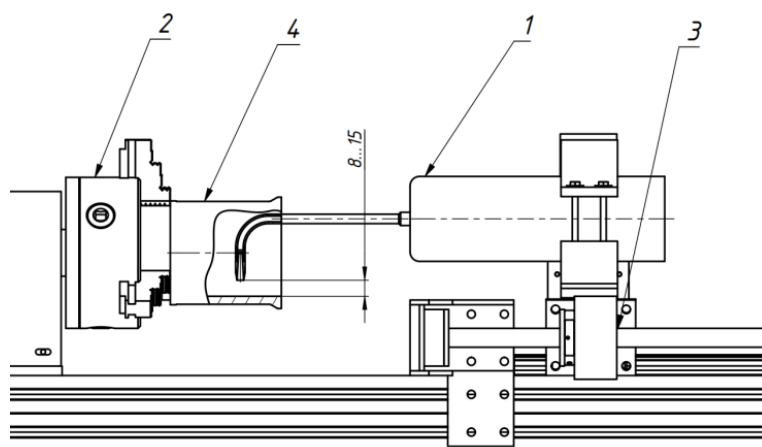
Эскиз автоматизированного комплекса для ХГДН гильз цилиндров:
